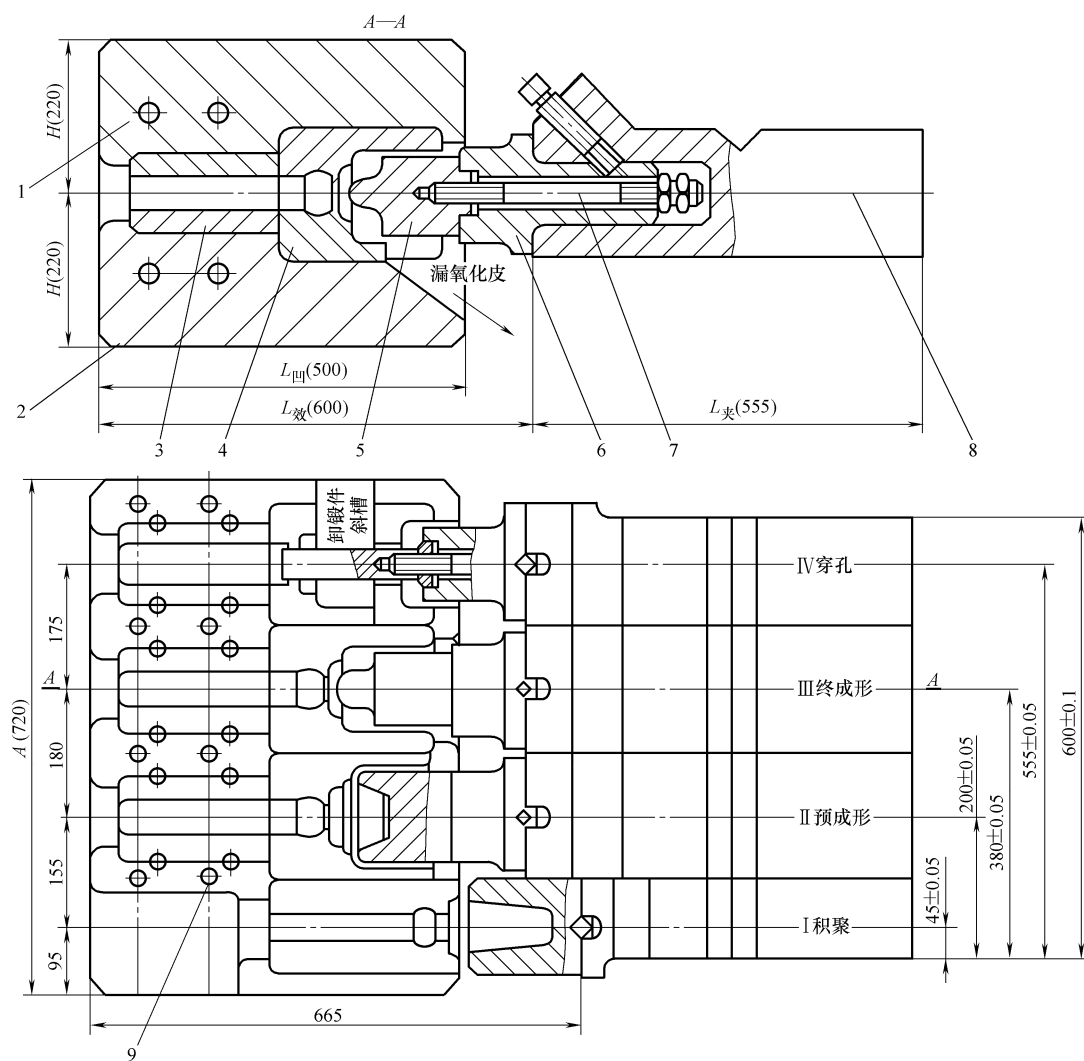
水平分模平锻机齿轮类模具 (9000kN 平锻机)
